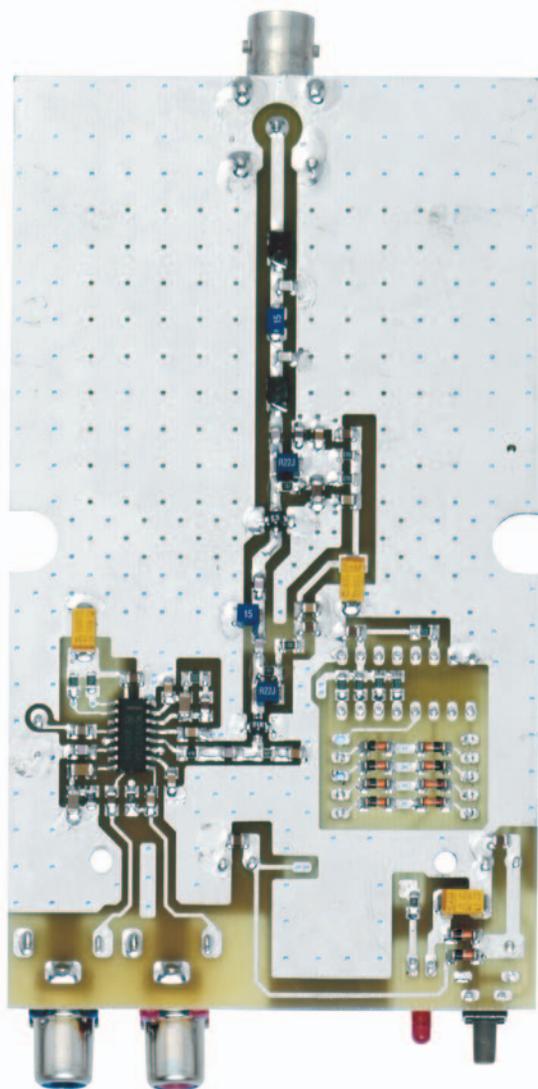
Photo d'un des prototypes de la platine vue du côté où sont soudés les CMS. Cette platine n'a pas à être réglée.
